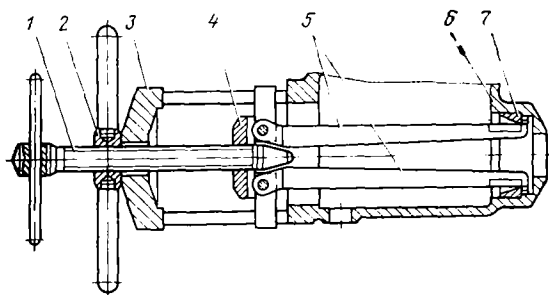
Съемник для выпрессовки наружного кольца конического подшипника из картера рулевого механизма:
